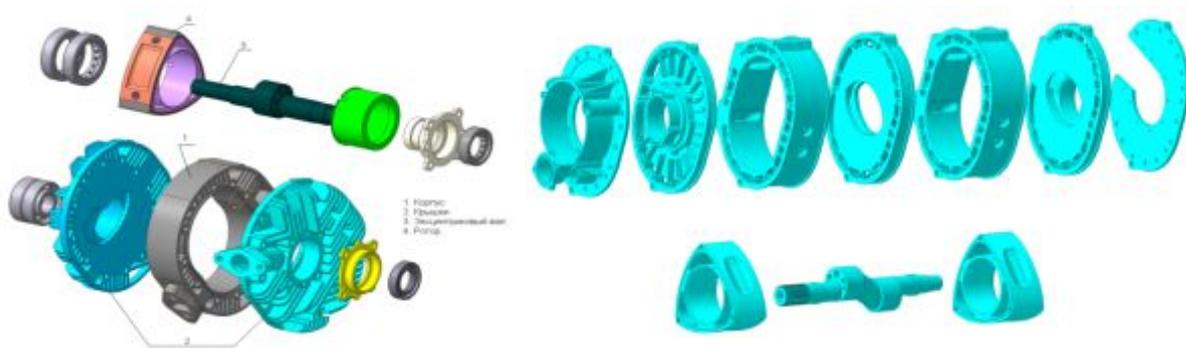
Основные детали модулей двигателей РПД-8 и РПД-100
